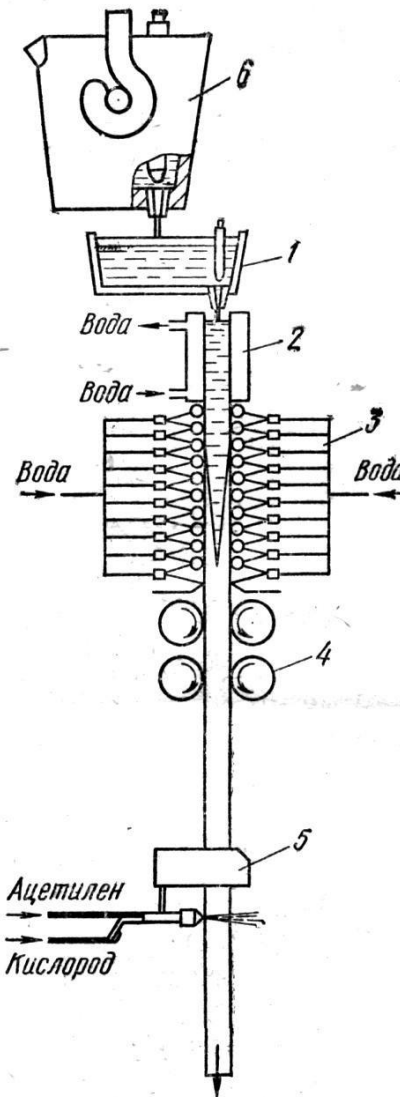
Схема установки для безперервного розливання сталі:
